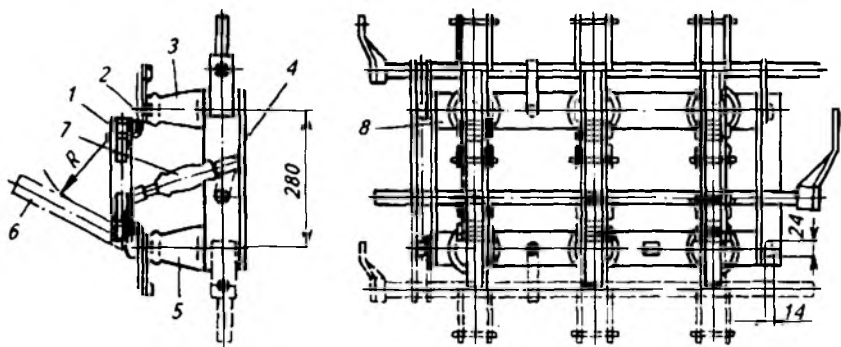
Схема разъединителя внутренней установки РВЗ/400
